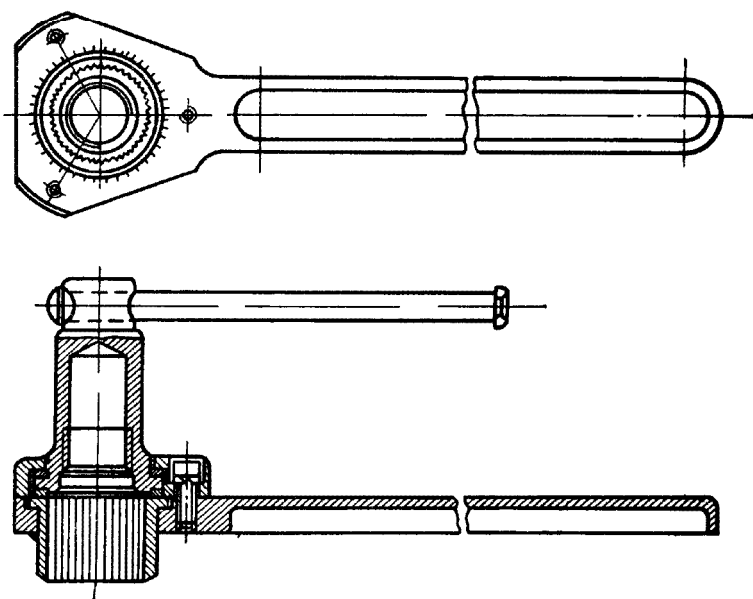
Общий вид рычажного ключа для поворота вала сошки
